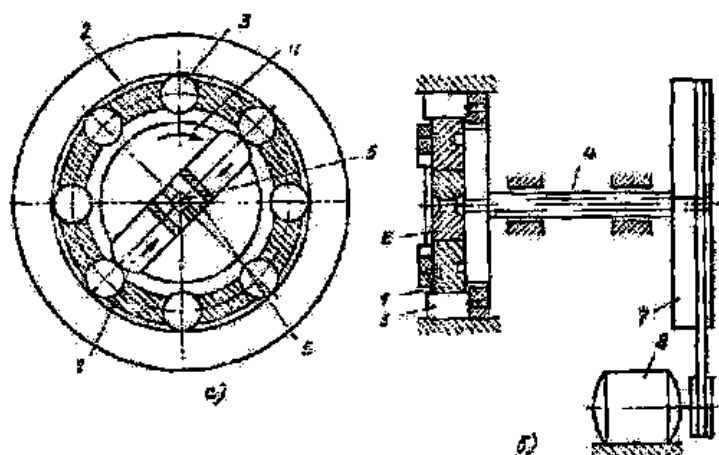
Ротационно-ковочная шпиндельная машина: 1 – ползуны; 2 – обойма; 3 – ролики; 4 – шпиндель; 5 – заготовка; 6 – бойки; 7 – клиноременная передача; 8 – электродвигатель.
